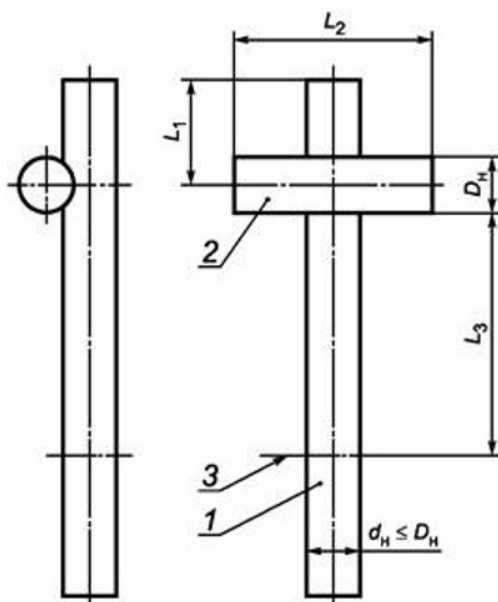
Схема испытаний крестообразных соединений на сдвиг
